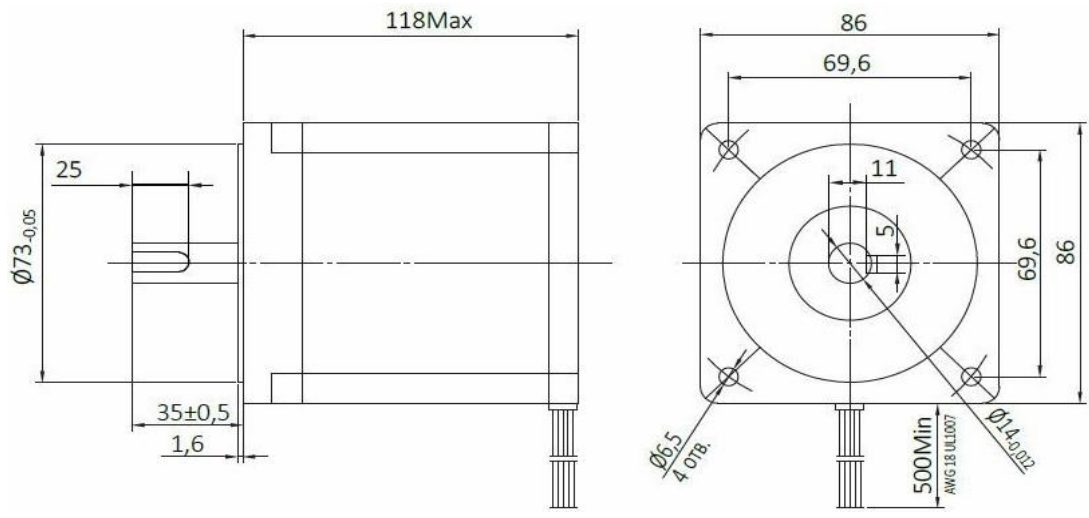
Габариты шагового двигателя FL86STH118-6004A
